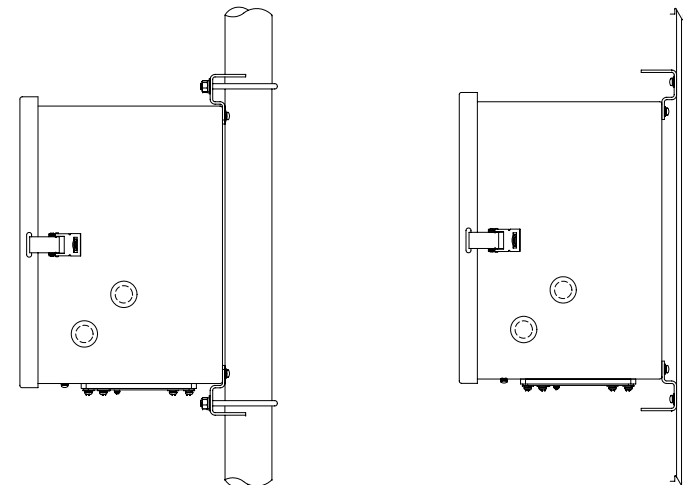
(Montagem da Tubulação ou Painel da OEU 6270)
